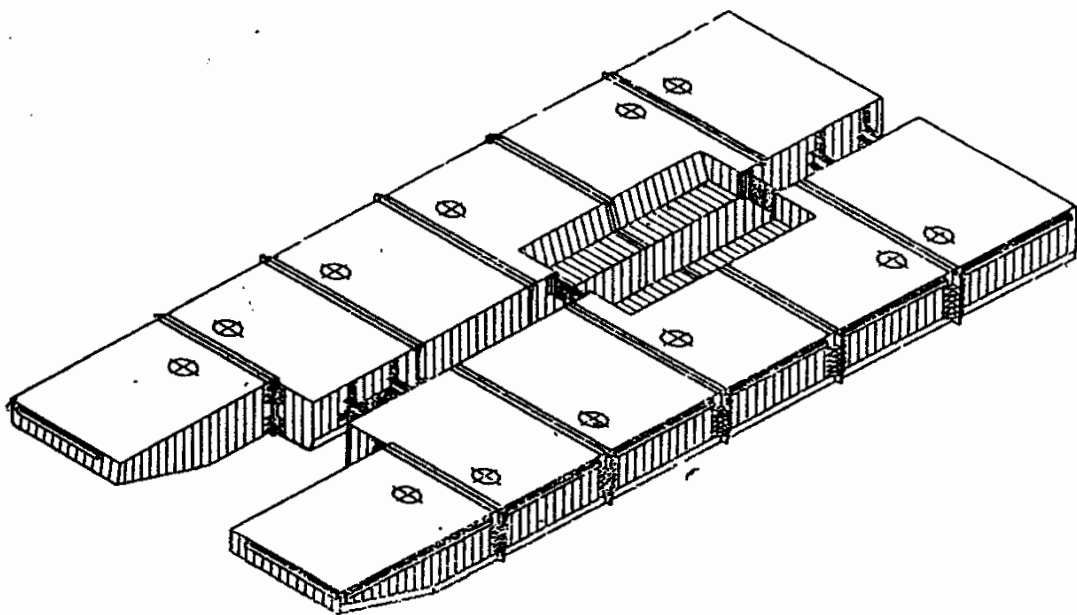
Общий вид корпуса земснаряда типа 12А-4.
